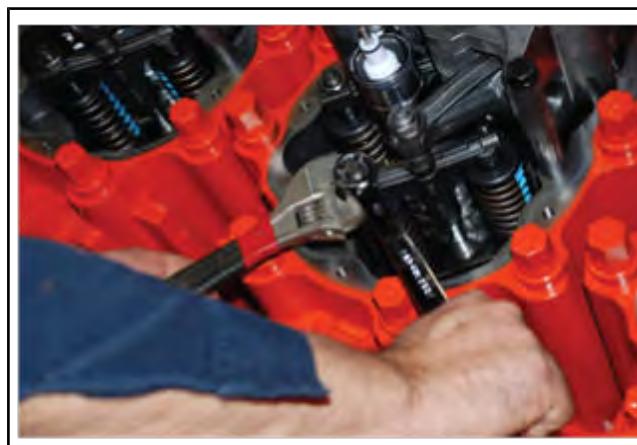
Настройка предварительного нагружения толкателя
